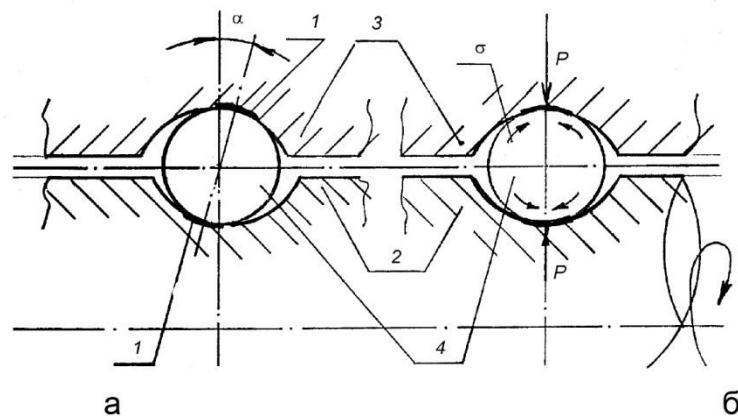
Схема обкатки шариков: а – изменение гравюры обкатного инструмента; б – схема обкатки шарика: 1 – площадка контакта шарика и инструмента, 2 – вращающаяся часть инструмента, 3 – неподвижная часть инструмента, 4 – шарик.
